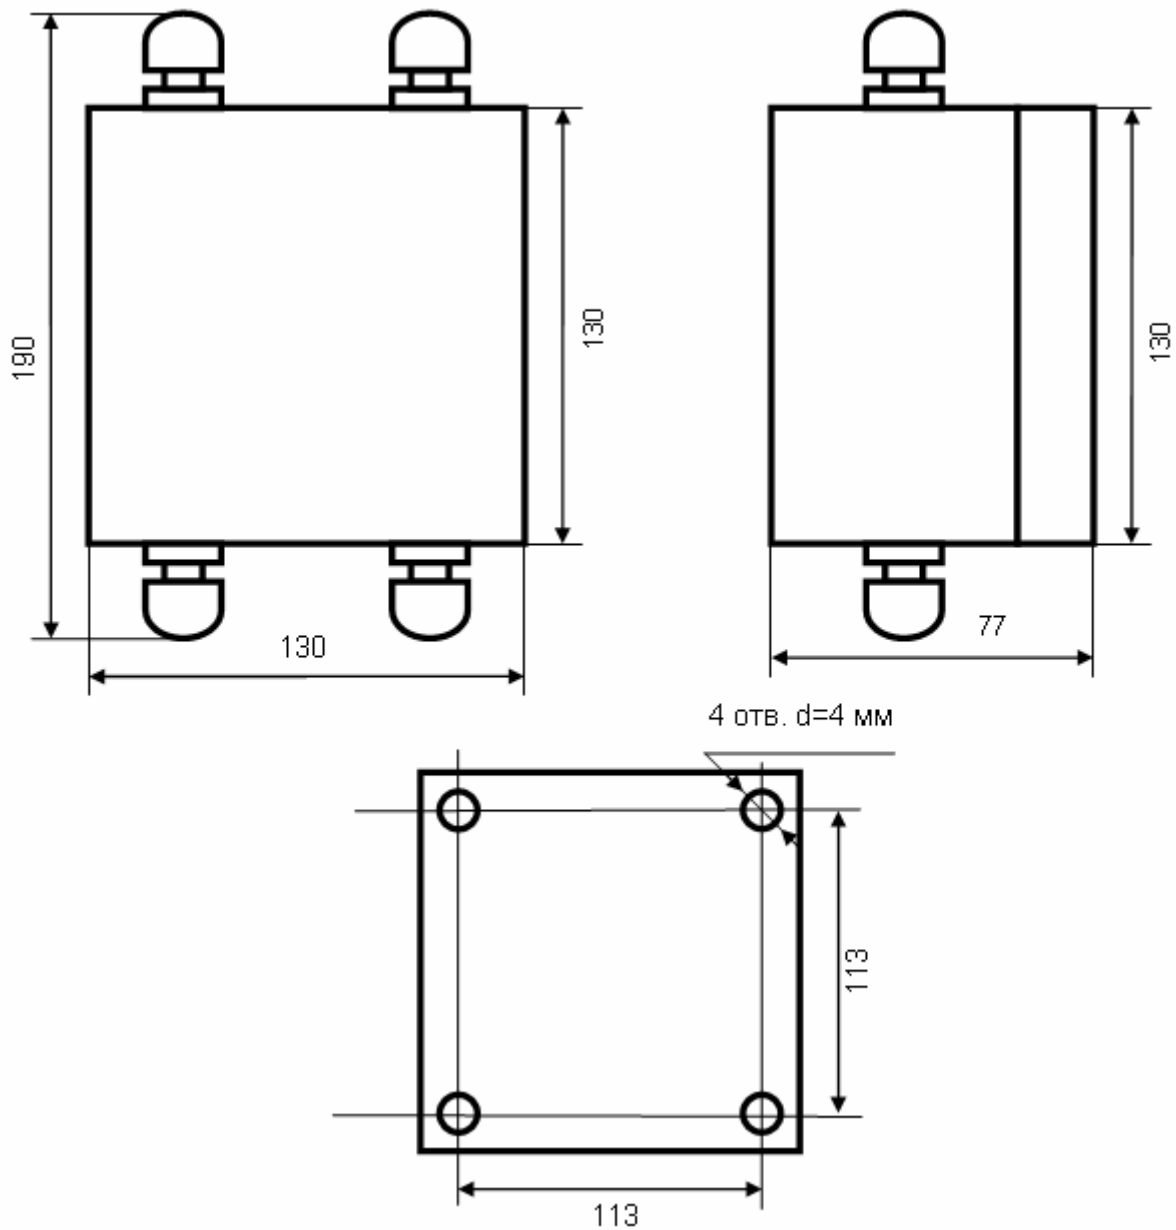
Габаритный чертеж контроллера в герметичном исполнении
